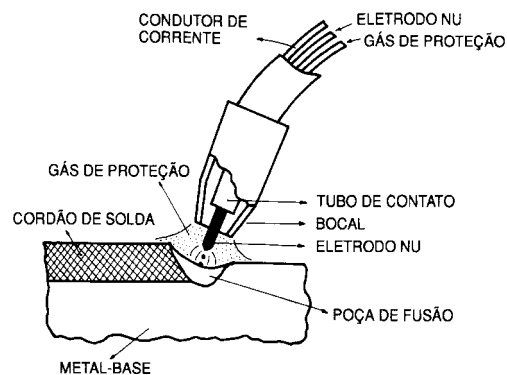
Processo de soldagem MIG/MAG (WAINER, 1995)
